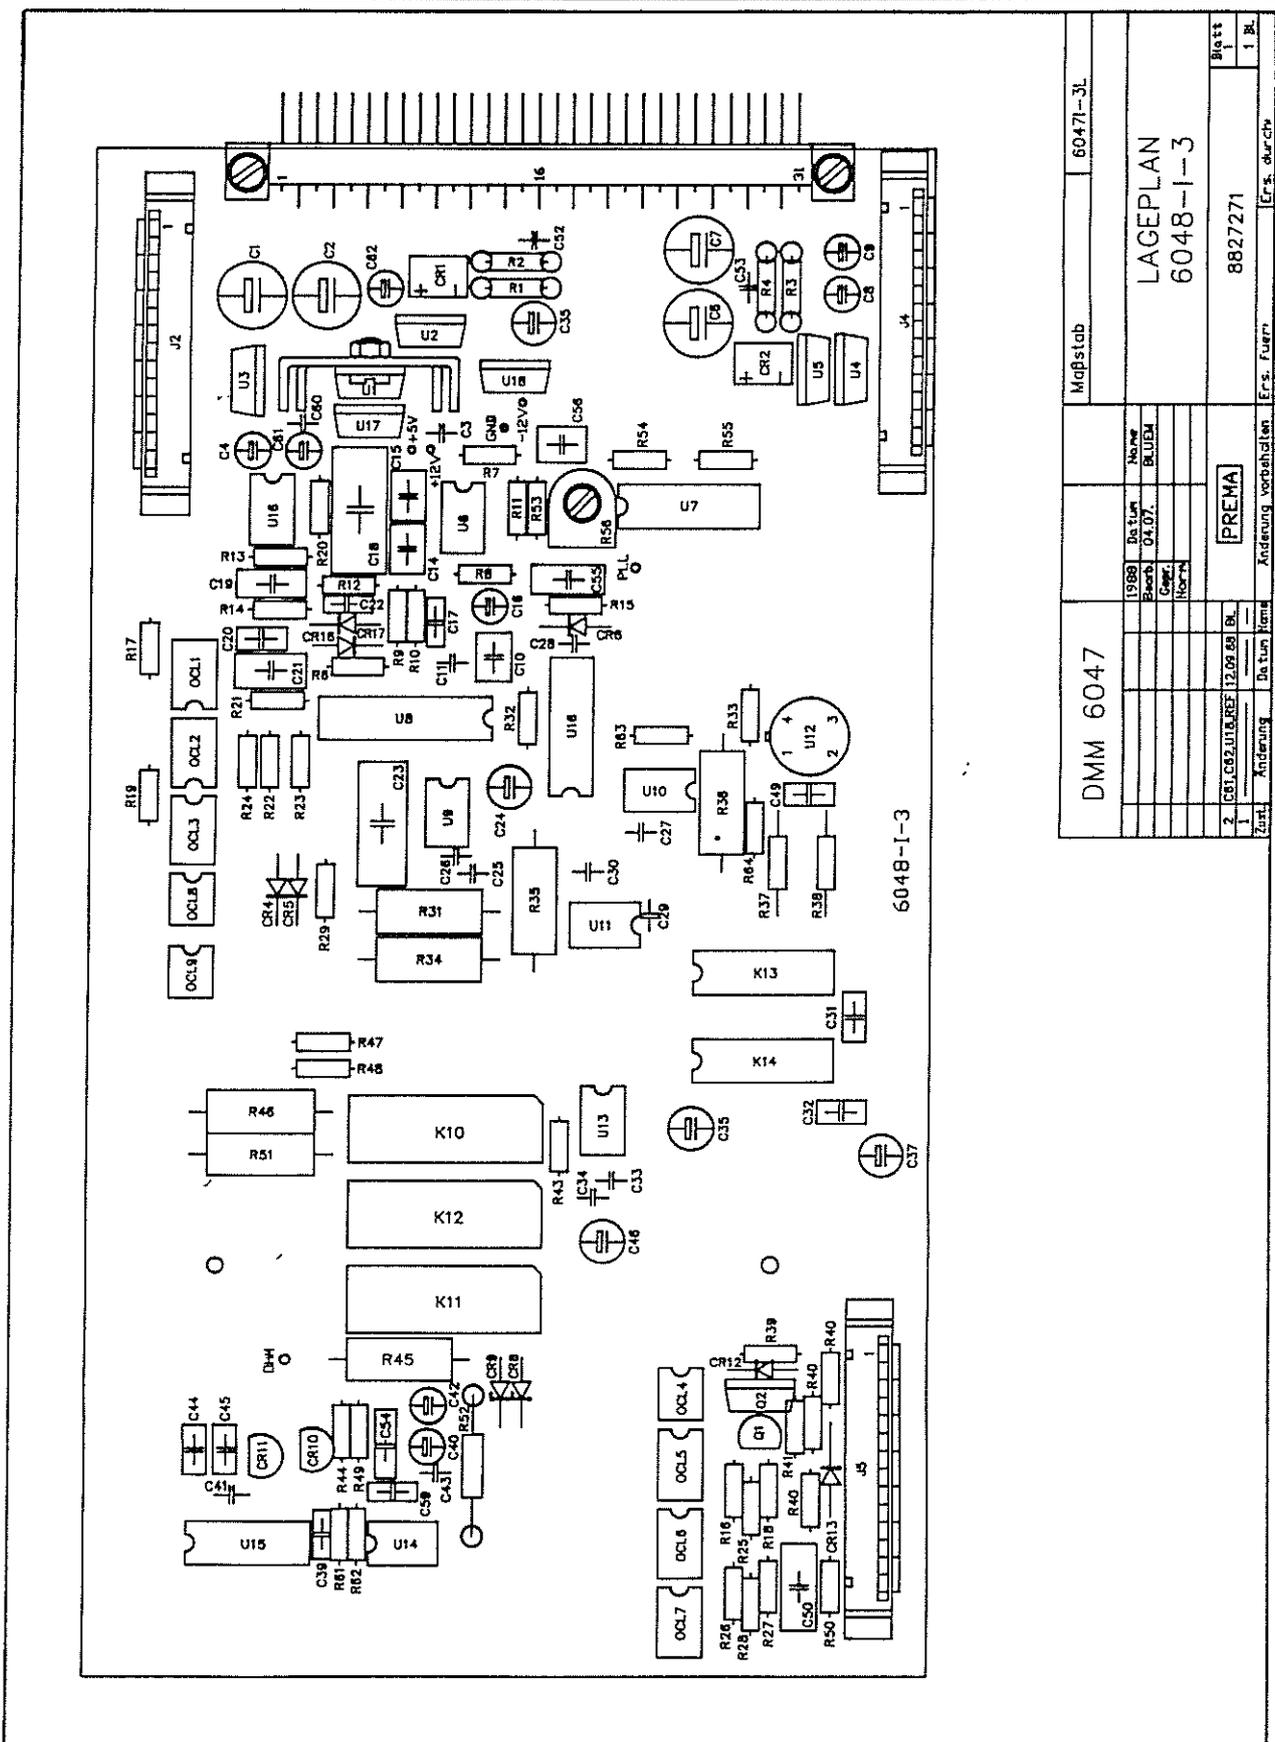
Lageplan der Integratorplatine DMM 6048
